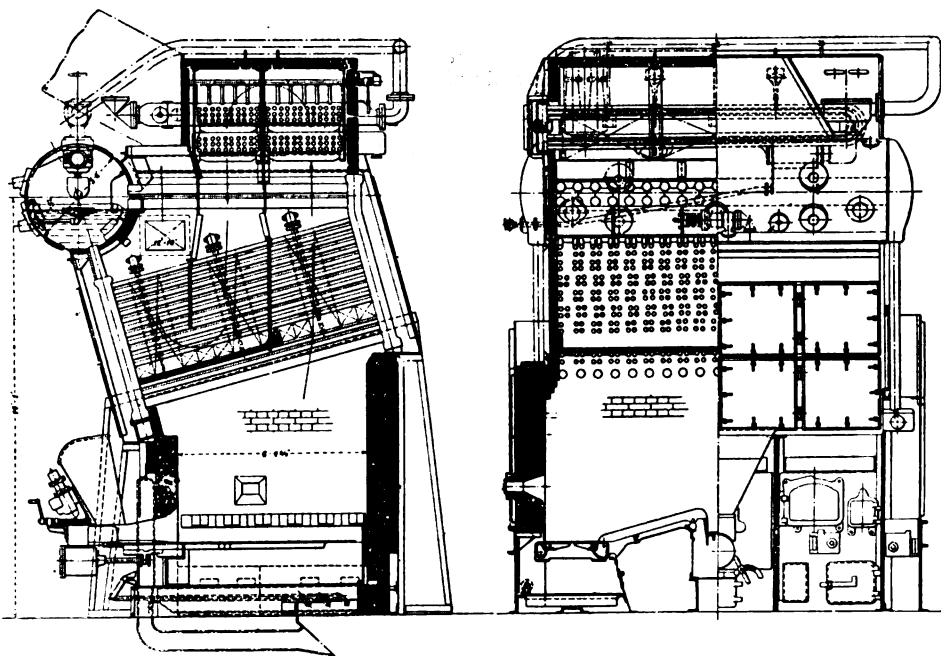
Babcock & Wilcox-Kessel mit Unterschubfeuerung
